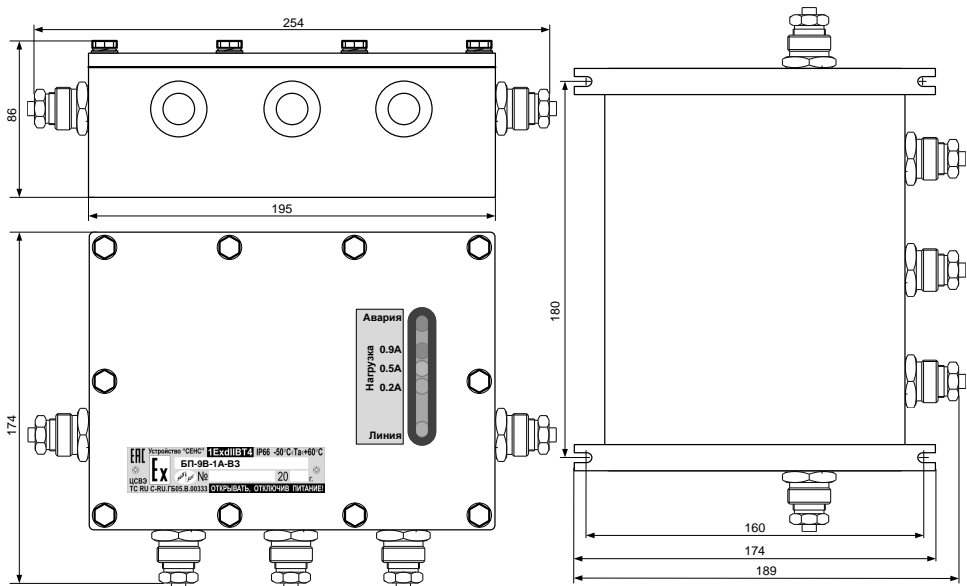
Внешний вид, габаритные и установочные размеры изделия взрывозащищённого исполнения
